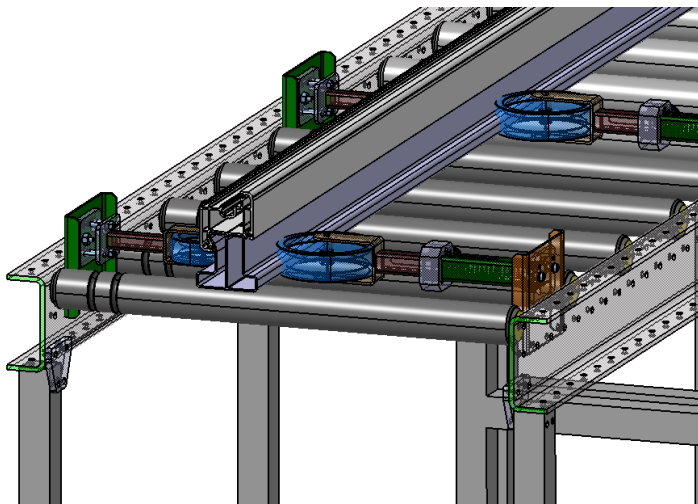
Detalhe em perspectiva do perfil P3051 + suporte no tapete de rolos – Pintura das 3 faces.
